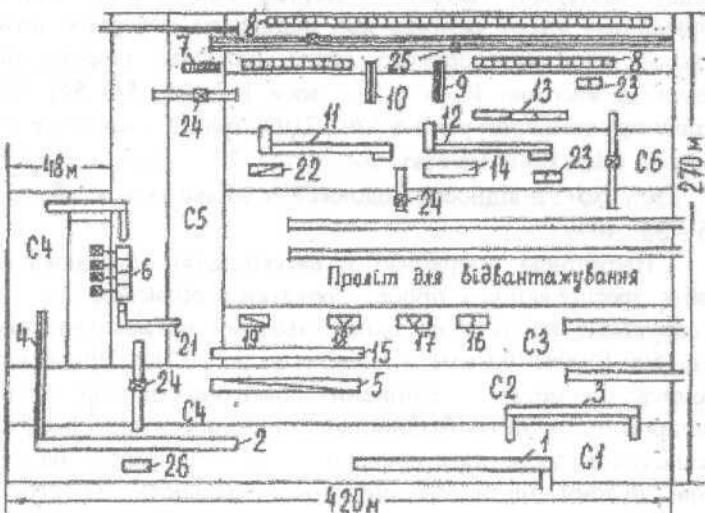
Схема розташування обладнання цеху холодної прокатки із неперервним чотирьохкліт'овим станом 1700: 1-підземний конвеєр рулонів; 2-неперервно-травильний агрегат; 3-агрегат нормалізації; 4-транспортер; 5-агрегат комбінованого різання; 6-четирьохкліт'овий стан; 7-конвеєр; 8-ковпакові печі для світлого відпалу рулонів; 9-конвеєр; 10-дресирувальний стан; 11, 12-агрегати поперечного різання; 13-агрегат поздовжнього різання; 14-агрегат сортування листів; 15-агрегат неперервного цинкування штаби; 16-стан з фігурними валками для випуску хвилястих листів; 17, 18-машини для упакування листів у пачки; 19-ножиці; 21-конвеєр; 22-ножиці; 23-ваги; 24, 25-передатні візки; 26-пакетизувальний прес; С1-склад гарячекатаних рулонів і листів; С2-склад гарячекатаних рулонів і листів; С3-склад оцинкованих листів; С4-склад травлених рулонів; С5-склад холоднокатаних рулонів; С6-склад готової продукції.
